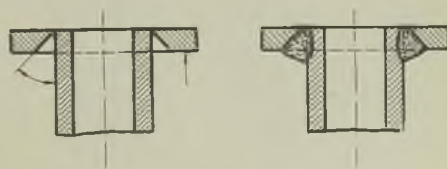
Anschweißen eines Flansches an einen Rohrflanschen: a) Vorbereitung (Abschrägen der Ränder und genaues Anpassen); b) Schweißung (im Flanschwinkel).
